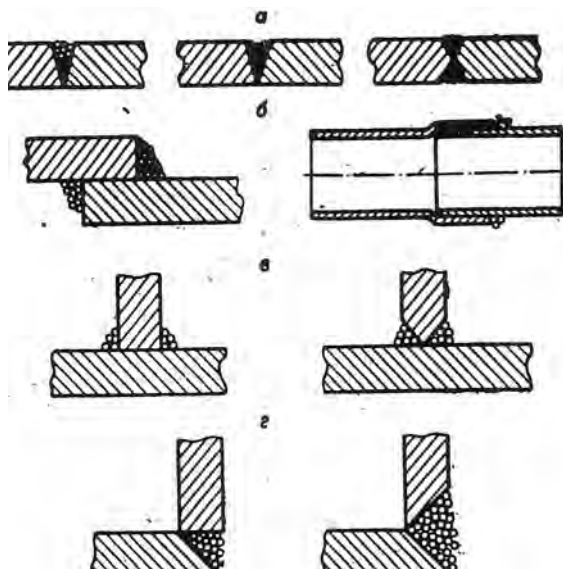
Типы сварных пластмассовых соединений:
